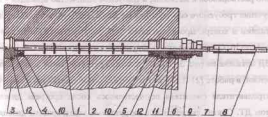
Схема смесителя для приготовления МГЭ в ТНВД УТН-5: 1 - вал смесителя; 2 - мешалка; 3 - корпус насоса; 4 - опоры; 5 - штуцер; 6 - болт; 7 - муфта; 8 - вал электродвигателя; 9 - конграйва; 10 - шальник; 11 - шпильки; 12 - кольцо уплотнительное
